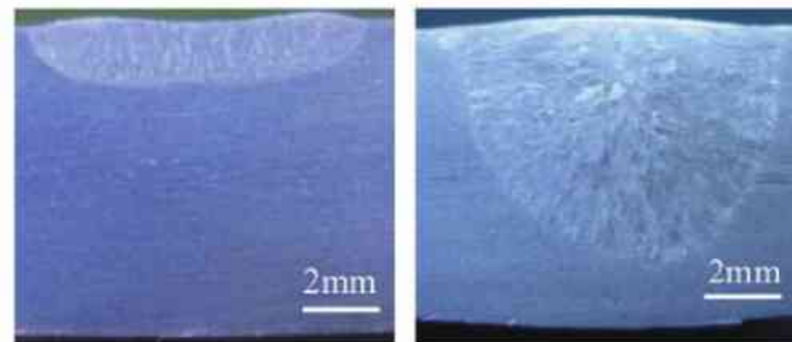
传统 TIG 焊和 AA-TIG 焊的熔深
